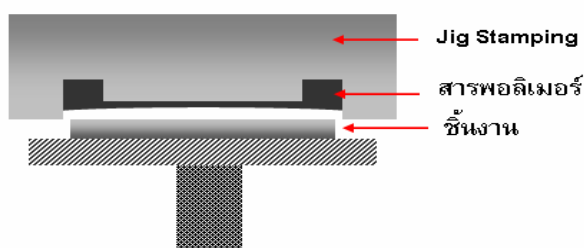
แสดง Jig Stamping แบบเดิม
